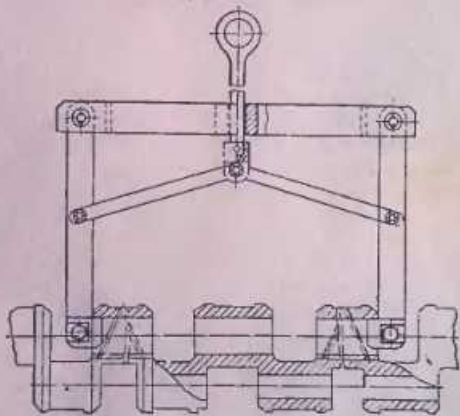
Приспособление ЛМ9690-048 для подъема колечатого вала
